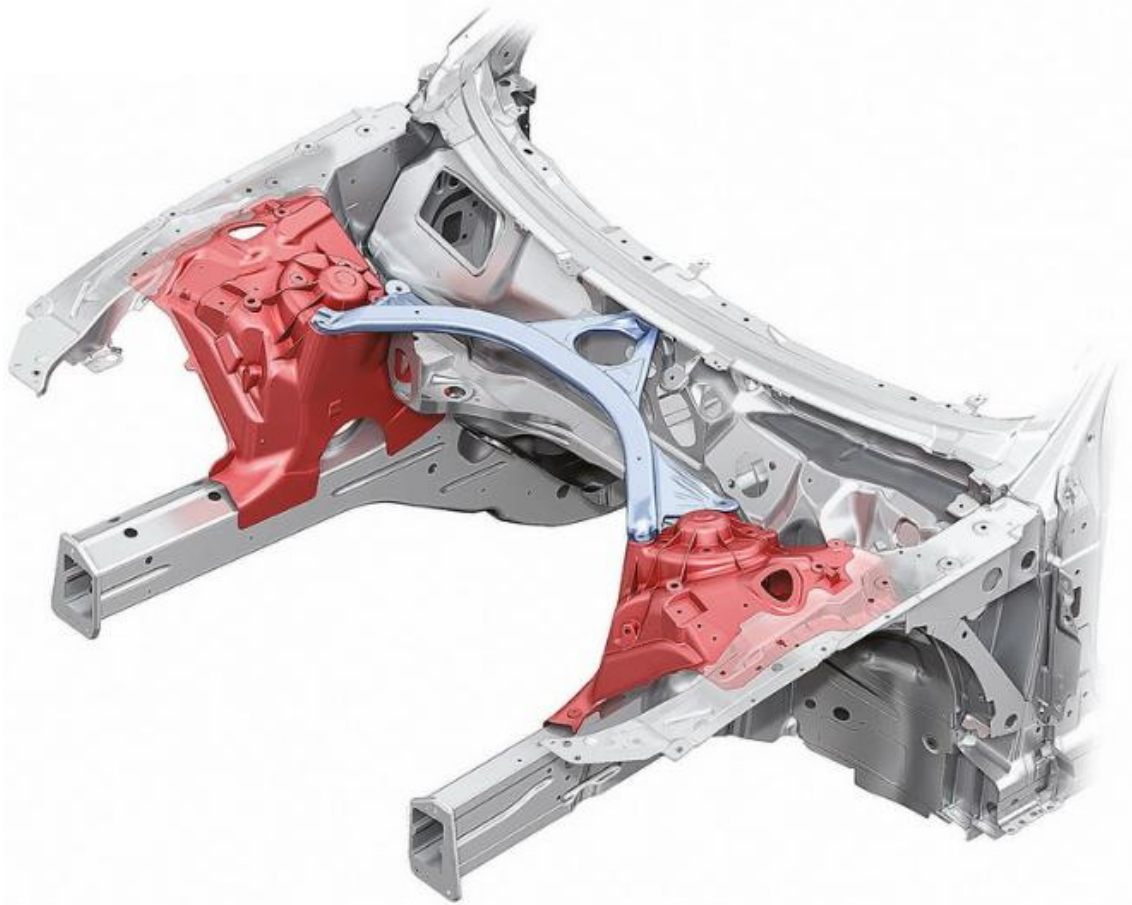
Montajes del soporte de la suspensión en aluminio fundido y puente de los soportes de la suspensión en aluminio en el Audi A6, [4].
